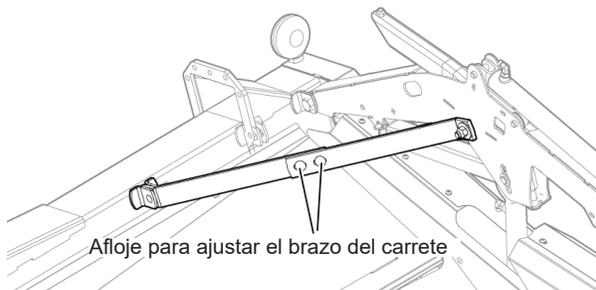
Centrado del carrete - soporte del brazo del carrete final
